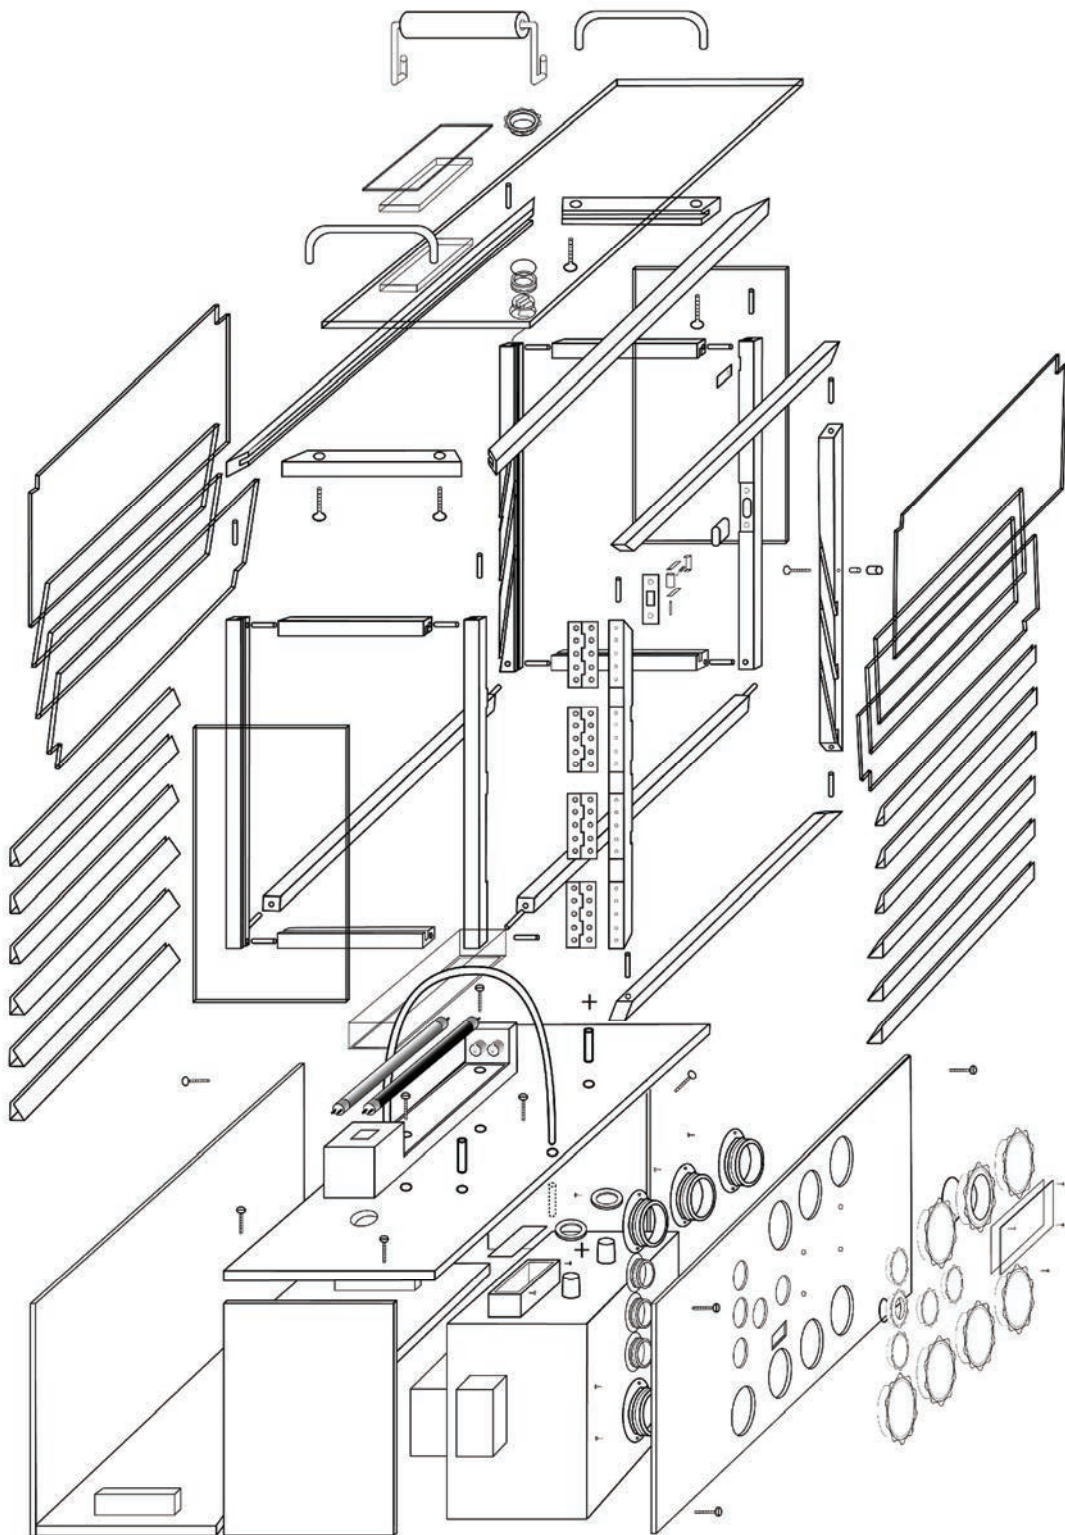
Dibujo tridimensional sin fuga del despiece de la trampa laminar sin incluir faldones.
